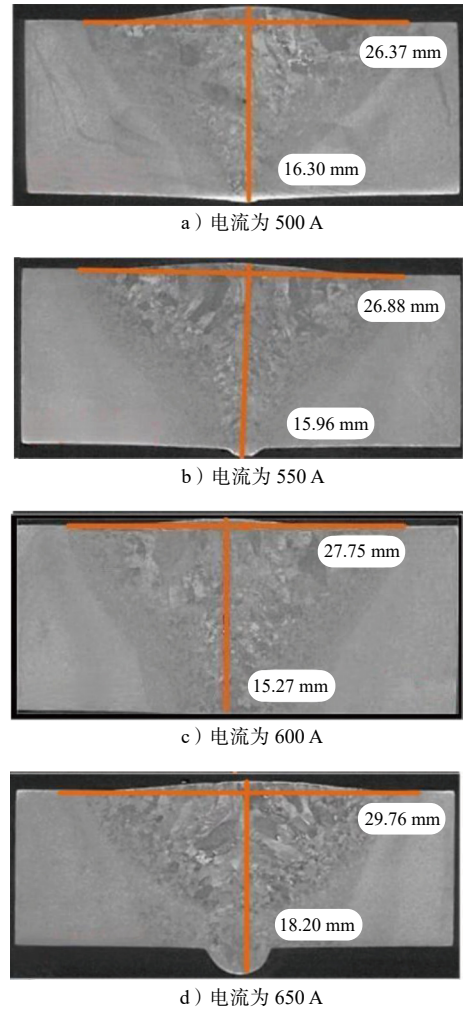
不同焊接电流条件下焊缝宏观形貌
